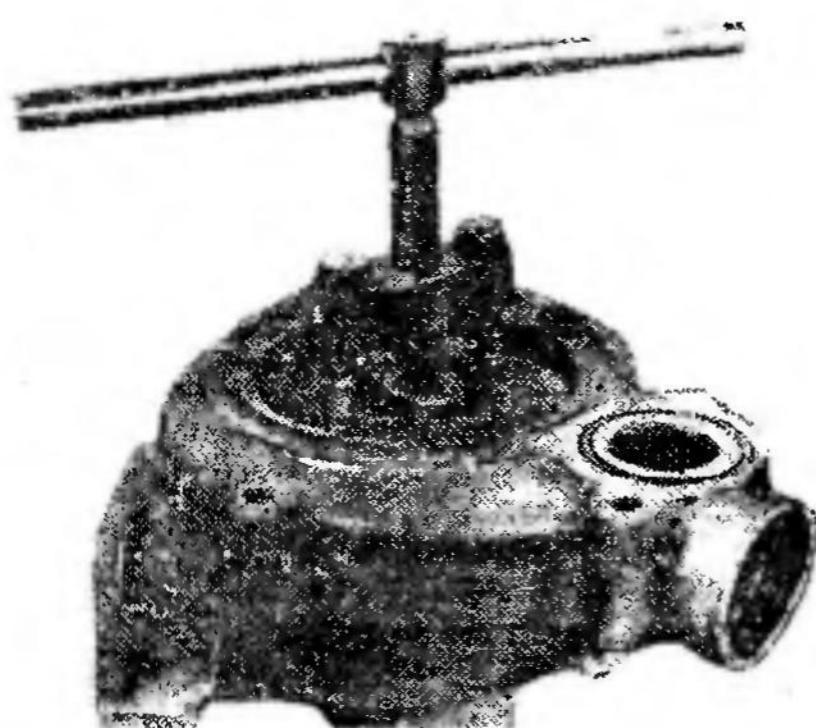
Снятие крыльчатки съемником подшипников карданных валов
